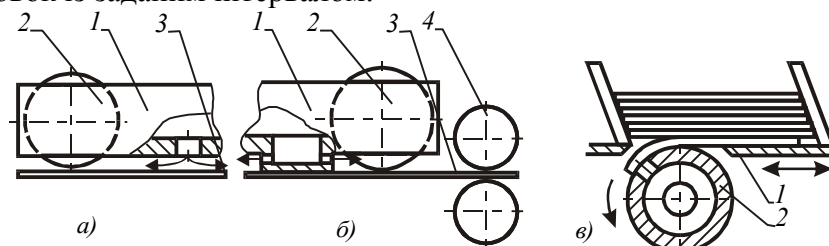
Струменеві механізми поштучного відділення листових заготовок.
